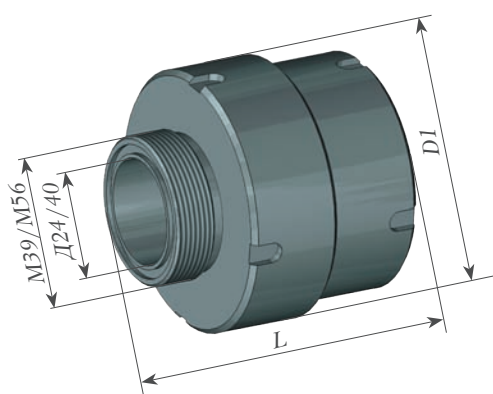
Общий вид клапана обратного модуля Ду 24, 40
